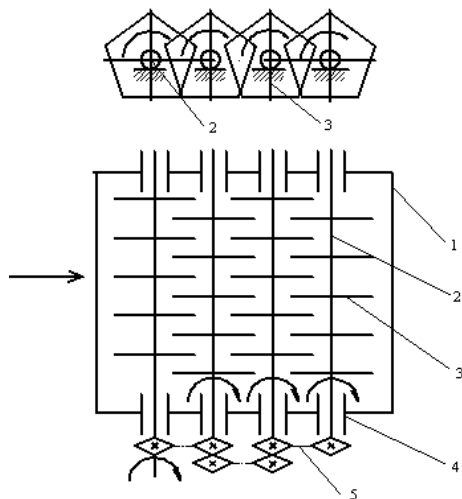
Схема трясильного апарата з фігурними пластинами; 1 – рама; 2 – вал; 3 – фігурна пластина; 4 – підшипникова опора; 5 – привід ланцюговий
